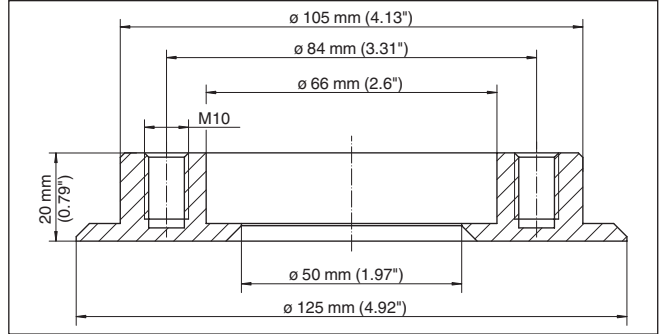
Maße Einschweißstutzen DRD - VEGABAR 82, 83
